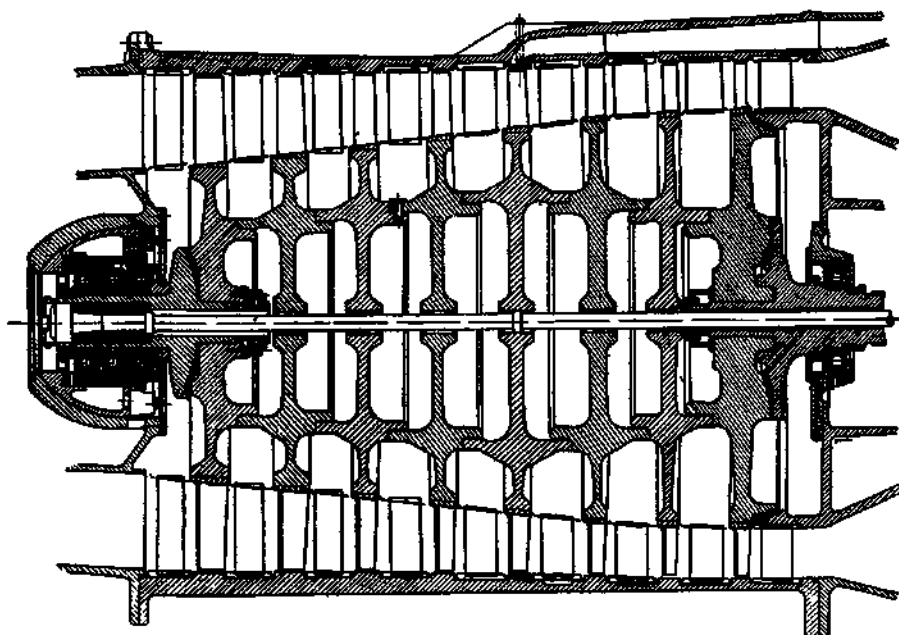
VII.—Compresor axial con rotor de discos del turboreactor Jumo 004.
